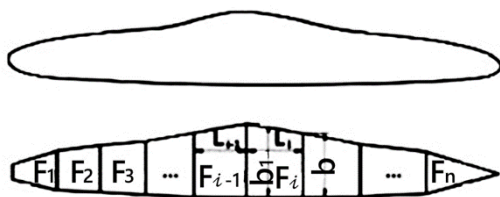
Схема к определению площади контактной поверхности вала с заготовкой при раскатке (прошивке): а – пятно контакта; б – аппроксимированное пятно контакта
